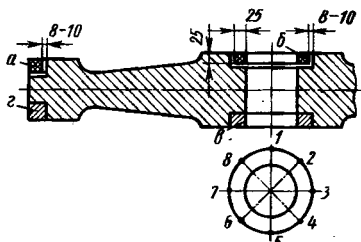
Схема вырезки образцов (колец) для испытания материала и определения внутренних напряжений в заготовке диска
